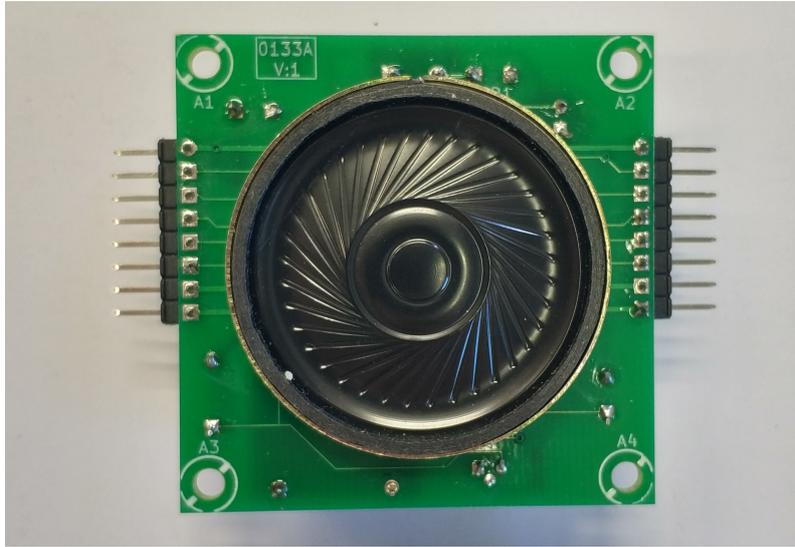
Montaje de la cara TOP del Módulo de Audio.
